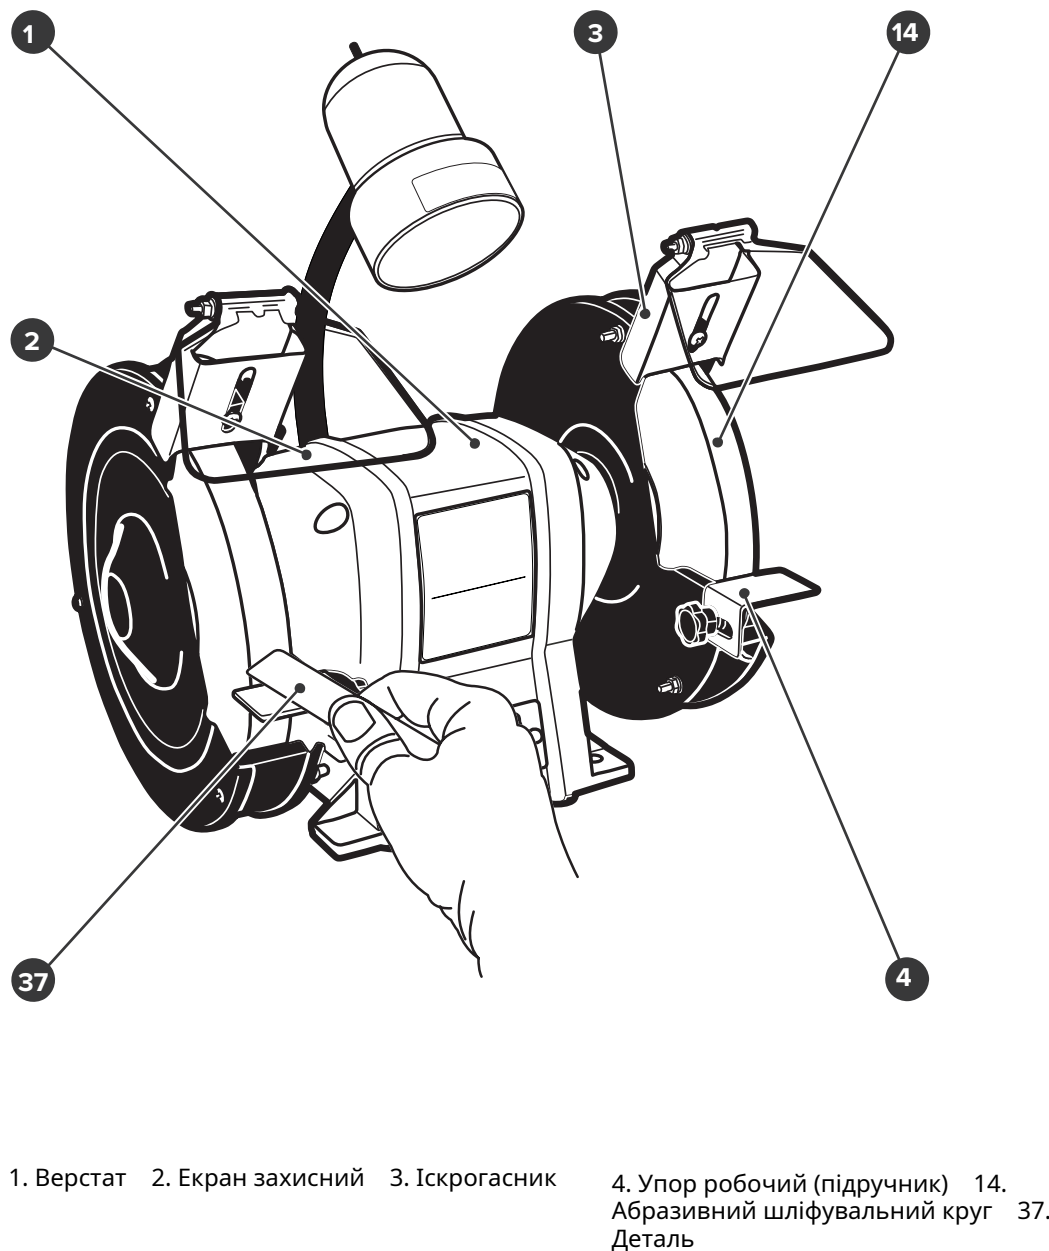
Приклад шліфування торця металевої деталі на верстаті
